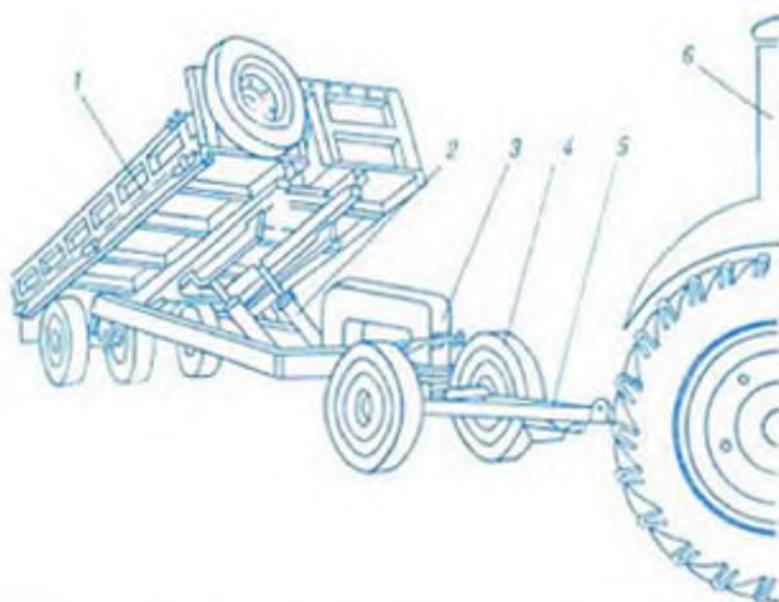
Прицепы. Прицеп для вывозки камней ПВК-5: 1 — кузов; 2 — гидроцилиндр подъёма кузова; 3 — рама; 4 — ходовые колёса; 5 — дышло; 6 — трактор.
